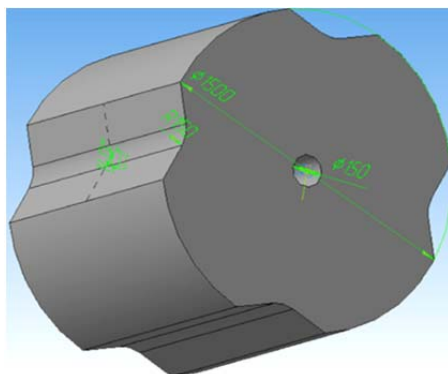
3D-модель профільованої заготовки на чотирипроменевої переріз
